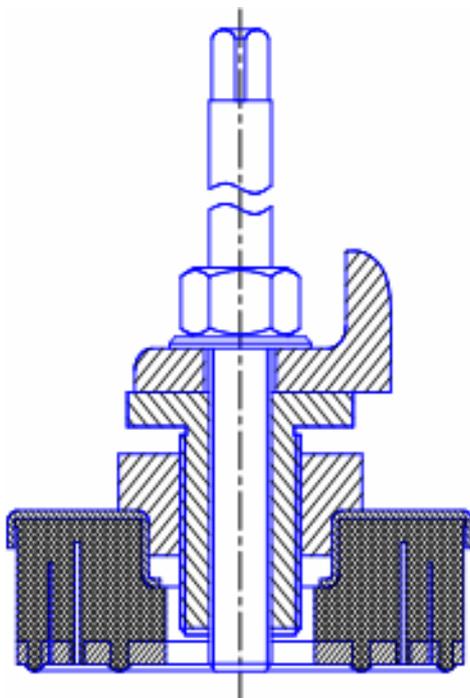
Конструкция упруго жесткой резинометаллической опоры
